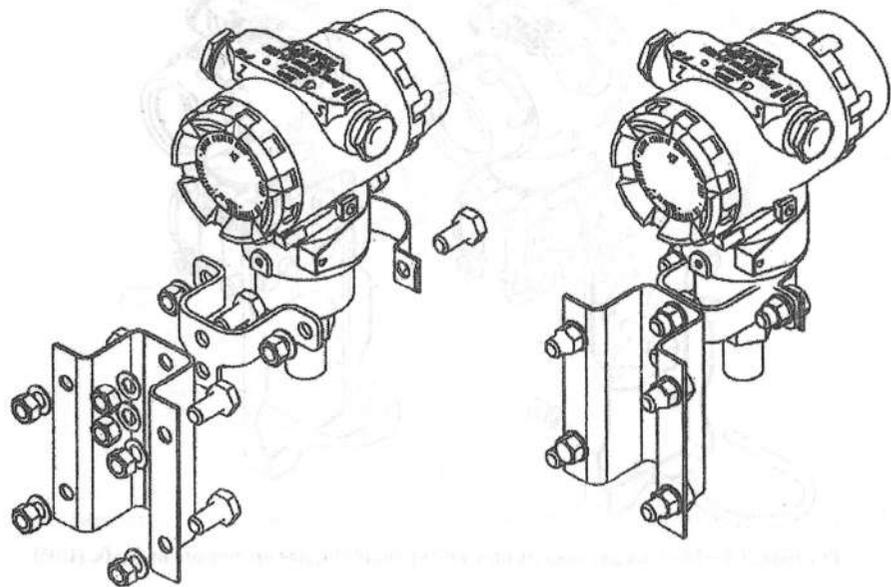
Монтаж датчика на кронштейн, для крепления на панели:
